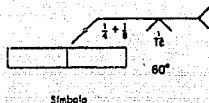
Símbolo de soldadura de acanaladura en "V" y soldadura que se desea obtener.
